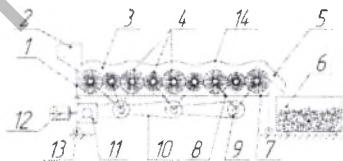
Схема устройства для очистки товарного картофеля: 1 – корпус; 2 – загрузочная воронка; 3 – рабочая камера; 4 – рабочие органы (вальцы); 5 – разгрузочная воронка; 6 – емкость; 7 – перфорированное днище; 8, 10 – цепная передача; 9 – звездочка; 11 – редуктор; 12 – электродвигатель; 13 – передвижные опоры; 14 – прорезиненное полотно
